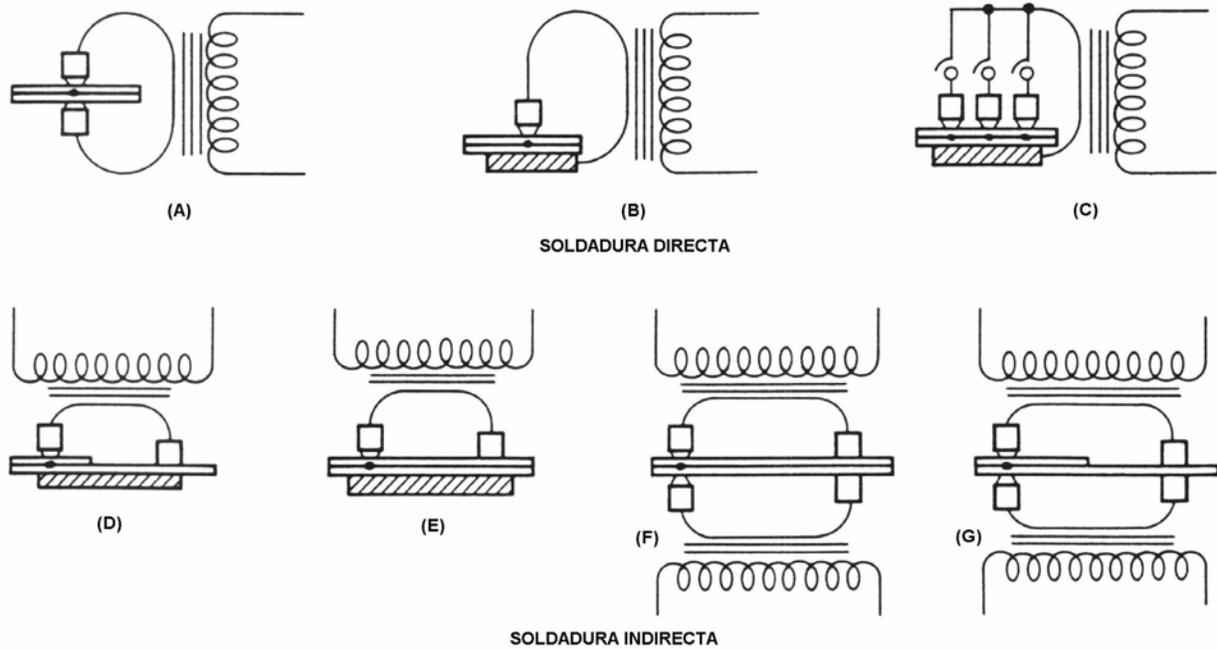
Arreglo Típico para Soldadura por Puntos Simples
